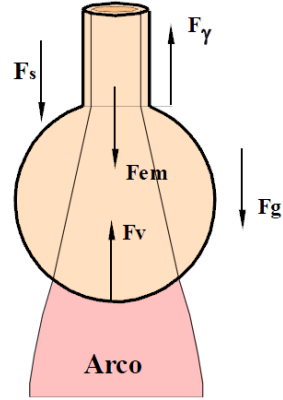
Forças que actuam na transferência de processos de soldadura MAG. Figura adaptada [12]
